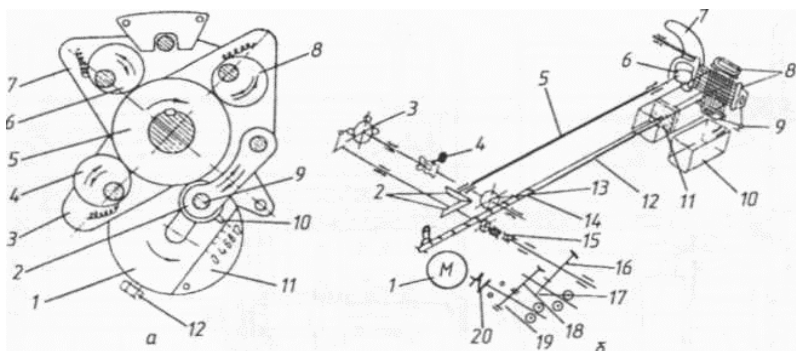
Механизм циклической подачи и кинематическая схема шпигорезки ФШМ-2:
